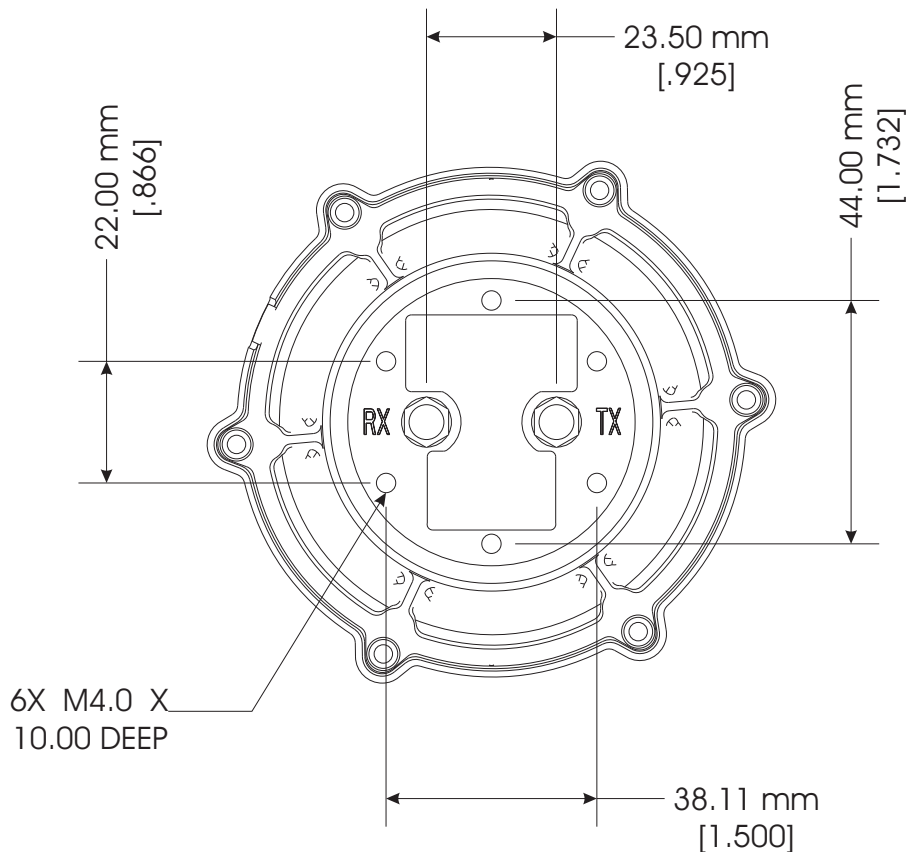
Вид Снизу DRA и Расположение Отверстий для Монтажа
